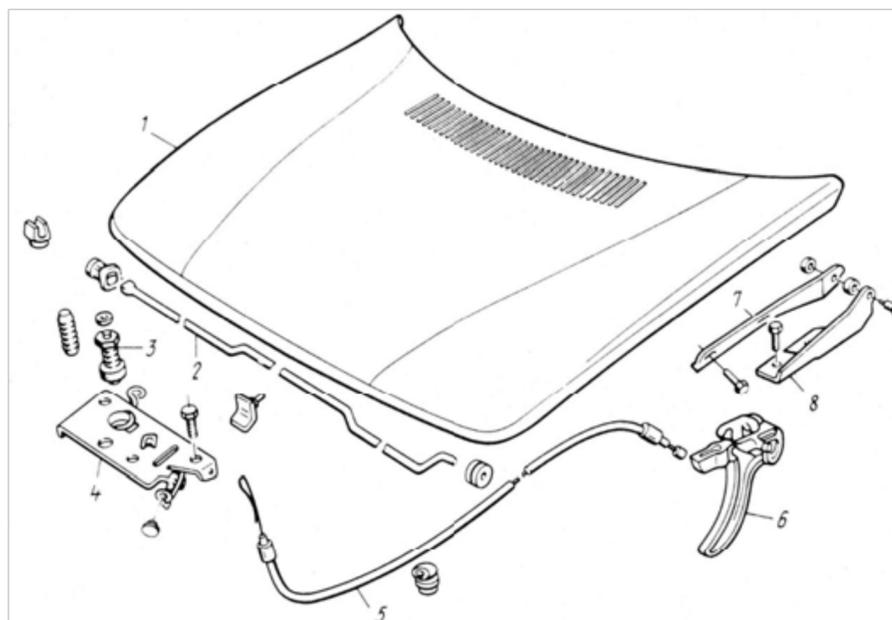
Капот двигателя автомобиля с механизмом открывания:
